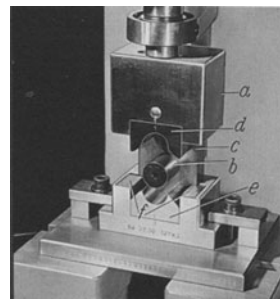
Umrollbiegewerkzeug mit im Oberteil verschieblicher Dornplatte
